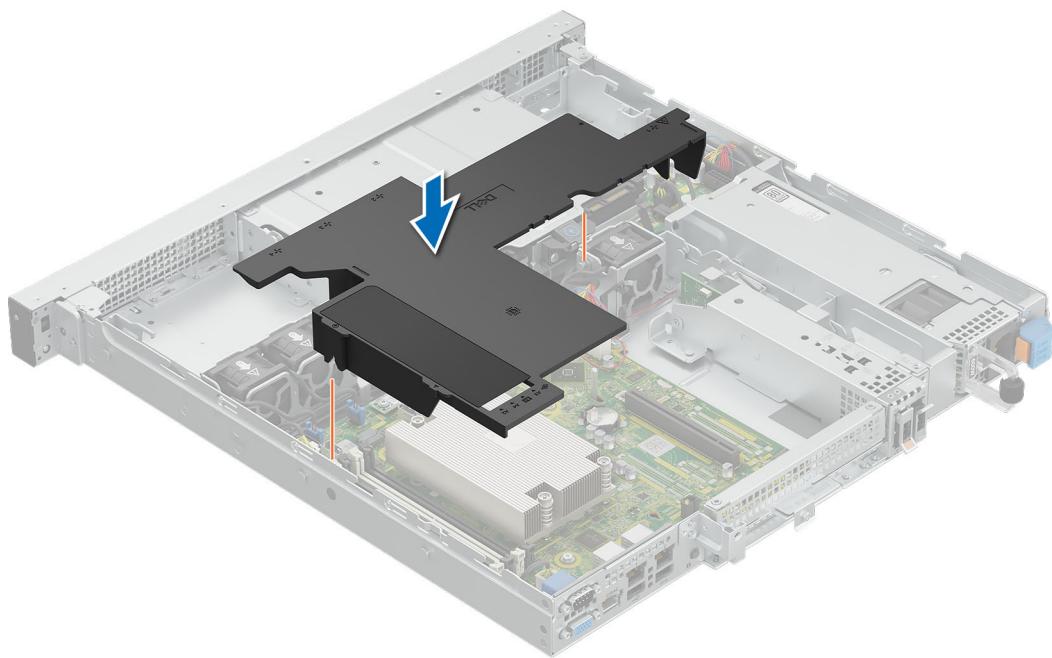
Installieren von Kühlgehäusen mit 3,5-Zoll-Laufwerken
